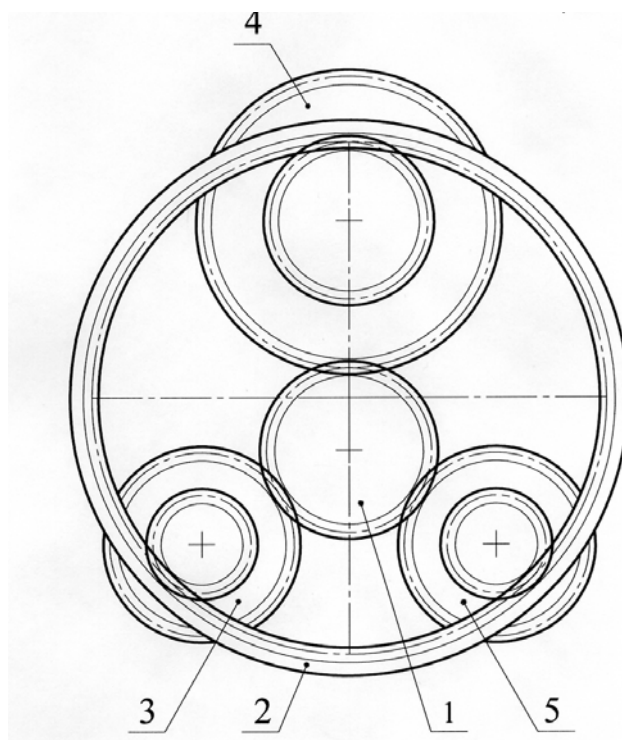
Зубчатый эксцентриковый подшипник
